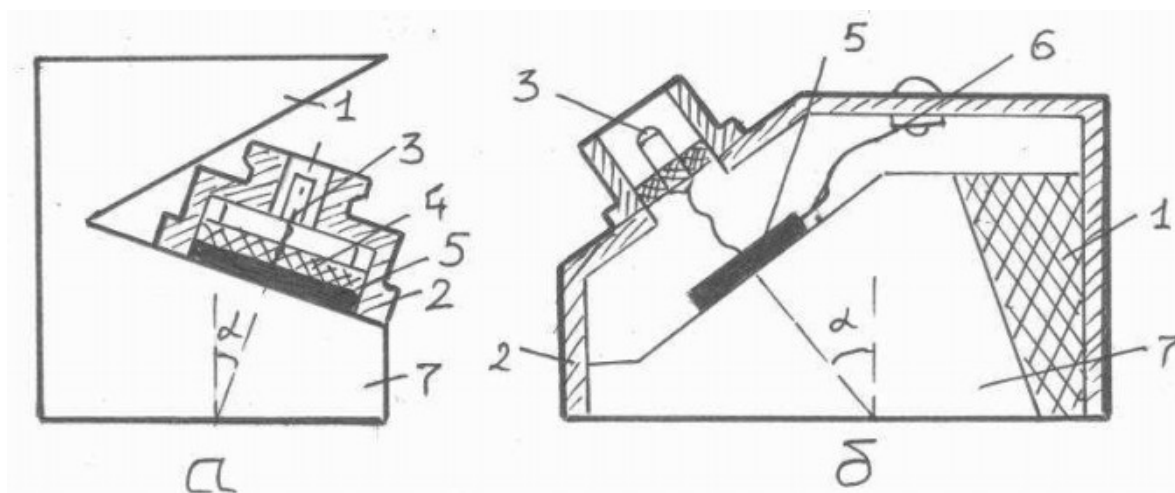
Наклонный преобразователь: 1, 7 – призма; 2 – корпус; 3 – предусилитель; 4 – протектор; 5, демпфер.
